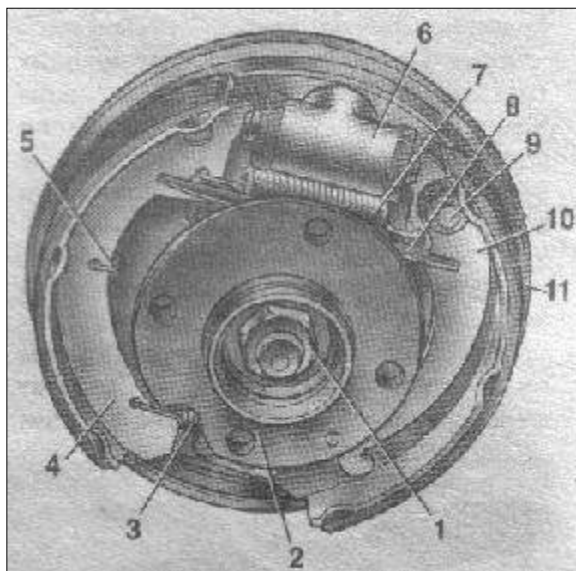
Гальмівний механізм заднього колеса: 1 – гайка кріплення маточини; 2 – маточина колеса; 3 – нижня стяжна пружина колодок; 4 – гальмівна колодка; 5 – напрямна пружина; 6 – колісний циліндр; 7 – нижня стяжна пружина; 8 – розтискна планка; 9 – палець важеля привода стоянкового гальма; 10 – важіль привода стоянкового гальма; 11 – щит гальмового механізму.
